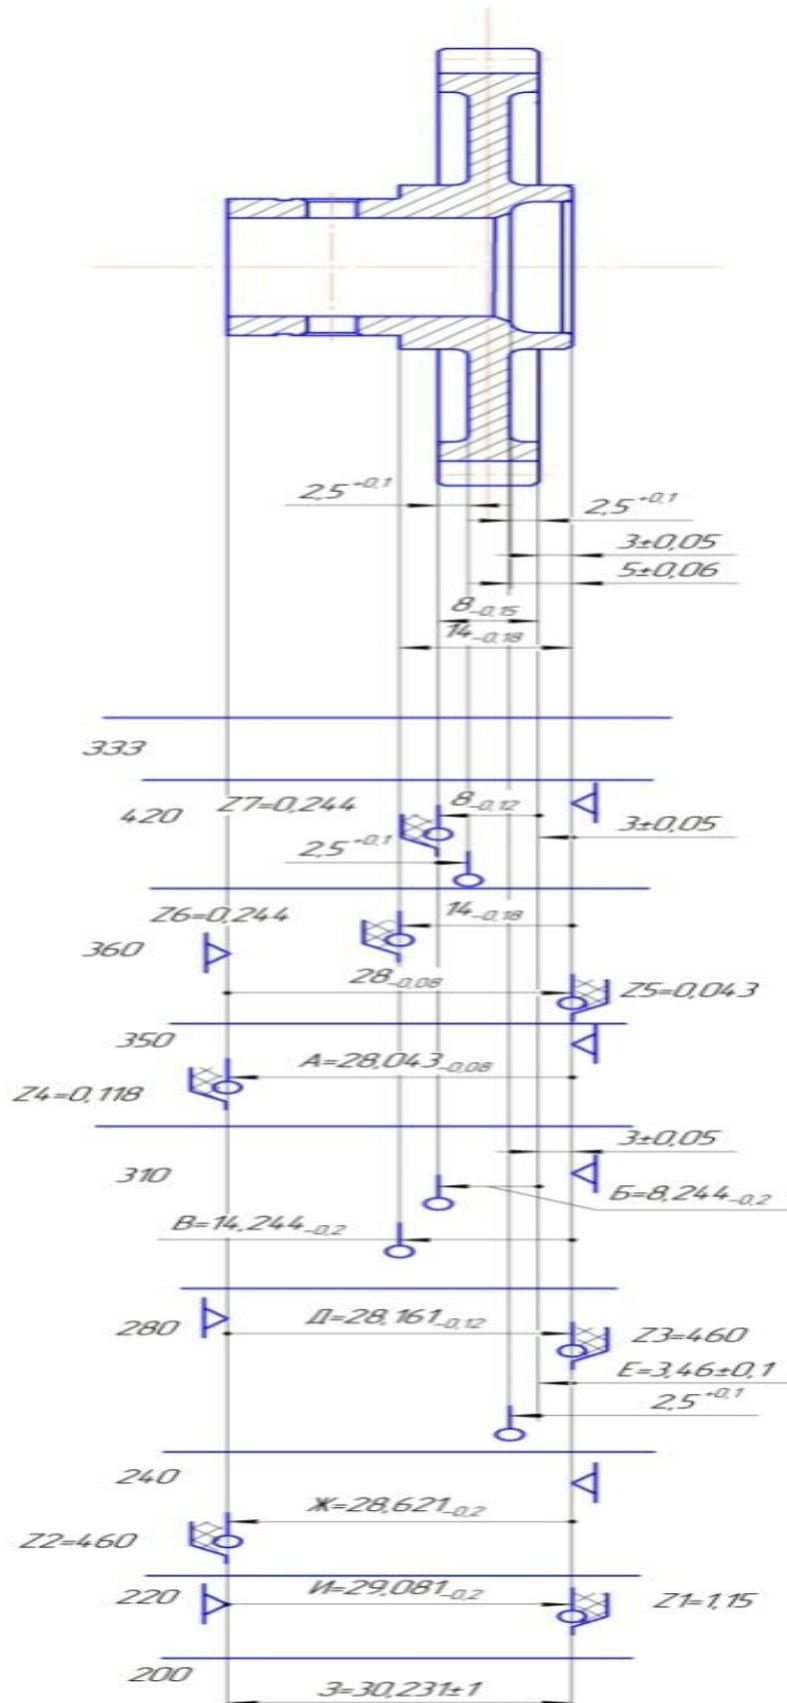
Размерная схема с технологическими припусками и размерами
